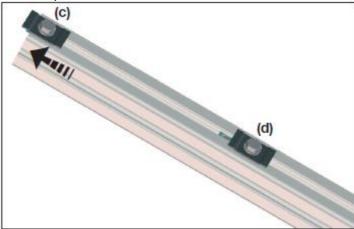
posizionare la guida al piede nella guida di montaggio
